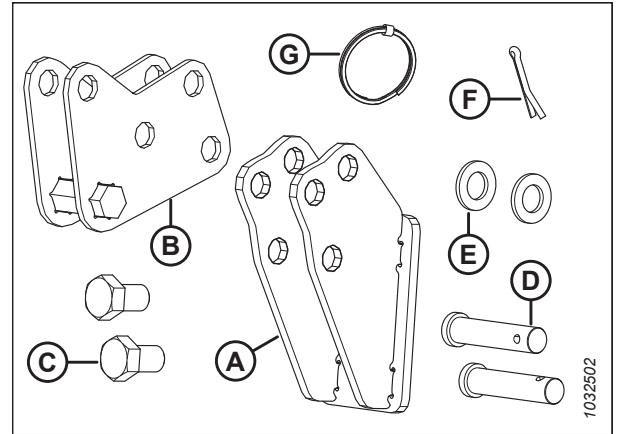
Sac de pièces pour le support avant-arrière MD № 347467
